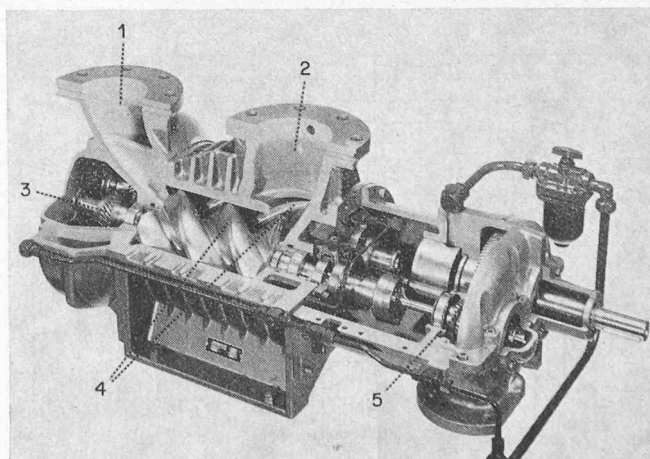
Modellbild eines Schraubenkompressors; 1 Ansaugstutzen, 2 Druckstutzen, 3 Synchronisiergetriebe, 4 Schraubenrotoren (nur der vordere Rotor ist deutlich sichtbar), 5 Übersetzungsgetriebe (Aerzener Maschinenfabrik GmbH, Aerzen/BRD)
